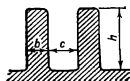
Ребра наружной поверхности корпуса закрытой обдуваемой машины.
